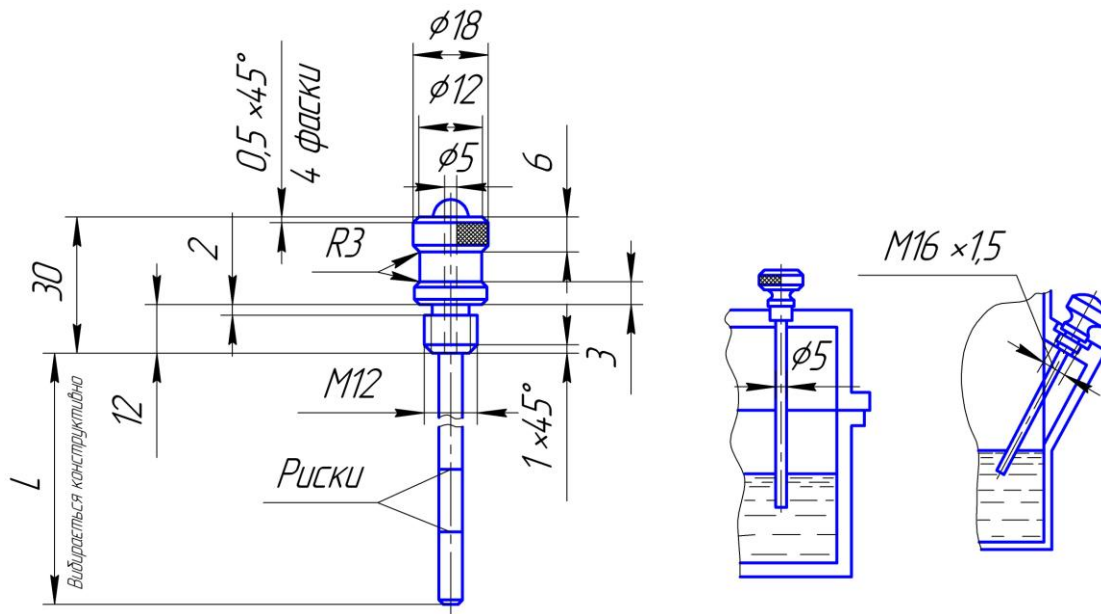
Жезловий показчик рівня масла і способи його установки на корпусі
